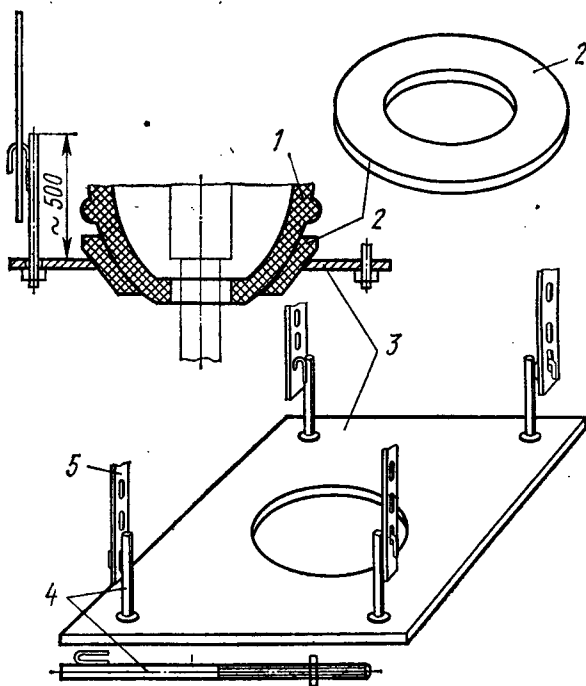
Приспособление для крепления нижней крышки к соединительной втулке ввода:
